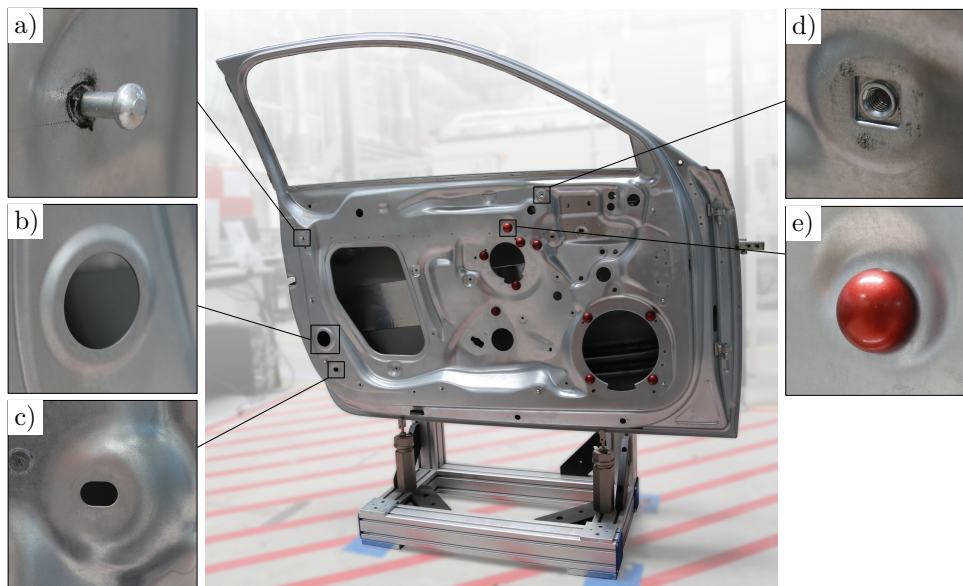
Prüfobjekt Autotür mit typischen Merkmalen: a) Bolzen, b) Bohrung, c) Langloch, d) Gewindebohrung, e) Messhilfsmittel für Gewindebohrung
